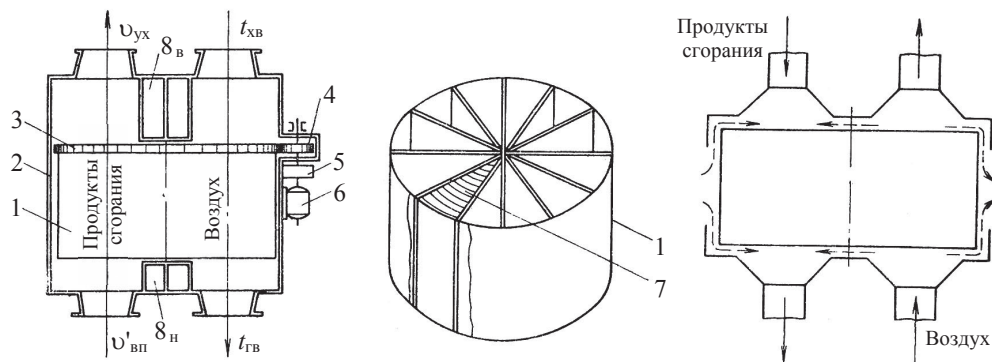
Регенеративный вращающийся воздухоподогреватель:
